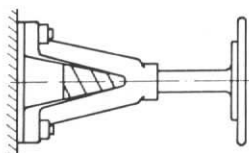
Stangenpuffer mit geschlossener Hülse.
